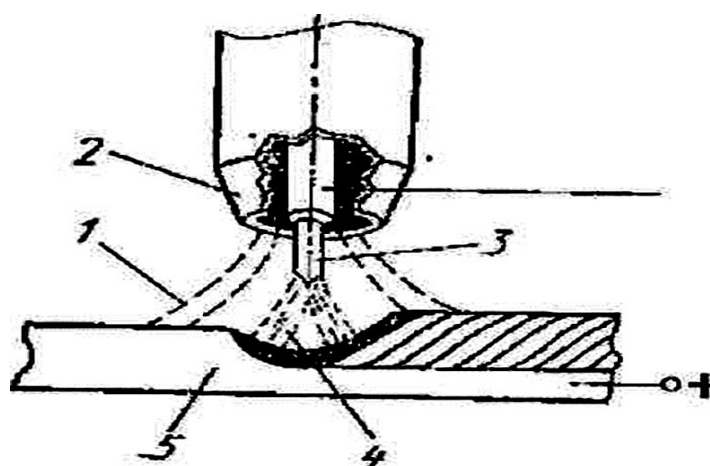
Схема дуговой сварки в атмосфере защитных газов:
